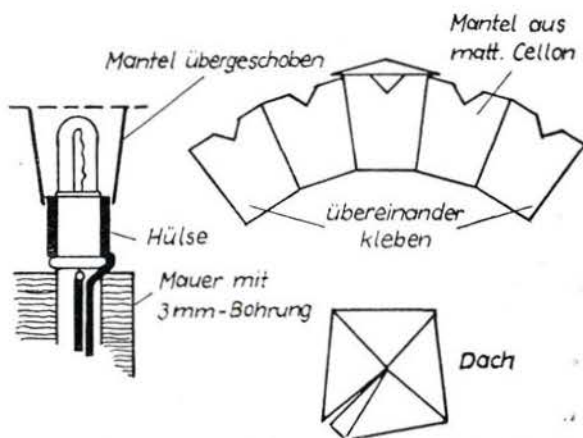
Laternen am Haupteingang (Maßstab 2 : 1)
